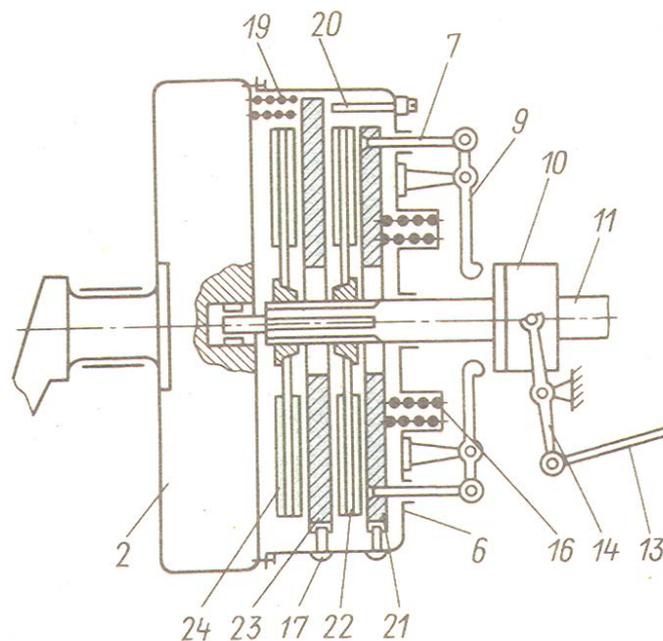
Сцепление двухдисковое: 2 – маховик; 7 – оттяжной палец; 9 – оттяжной рычаг; 10 – муфта выключения сцепления; 11 – ведущий вал; 13 – тяга; 14 – вилка выключателя; 16 – нажимная пружина; 17 – направляющий палец; 19 – отжимная пружина промежуточного диска; 20 – регулировочный болт промежуточного диска; 21 – нажимной ведущий диск; 22 – задний ведомый диск; 23 – промежуточный ведущий диск; 24 – передний ведомый диск
